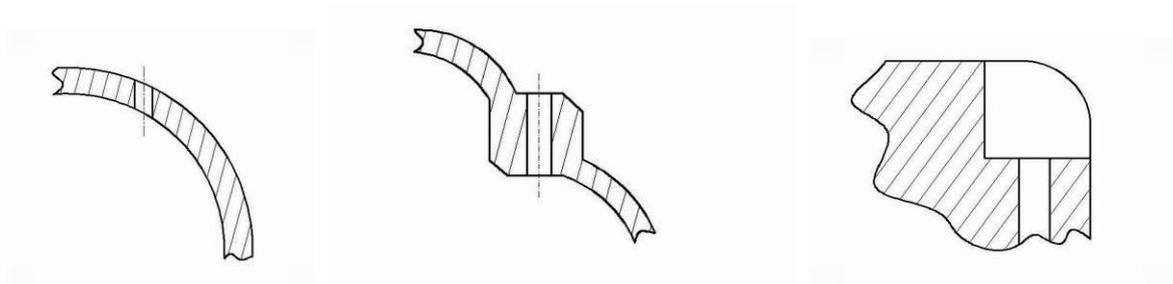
Требования к конструкциям обрабатываемых деталей
